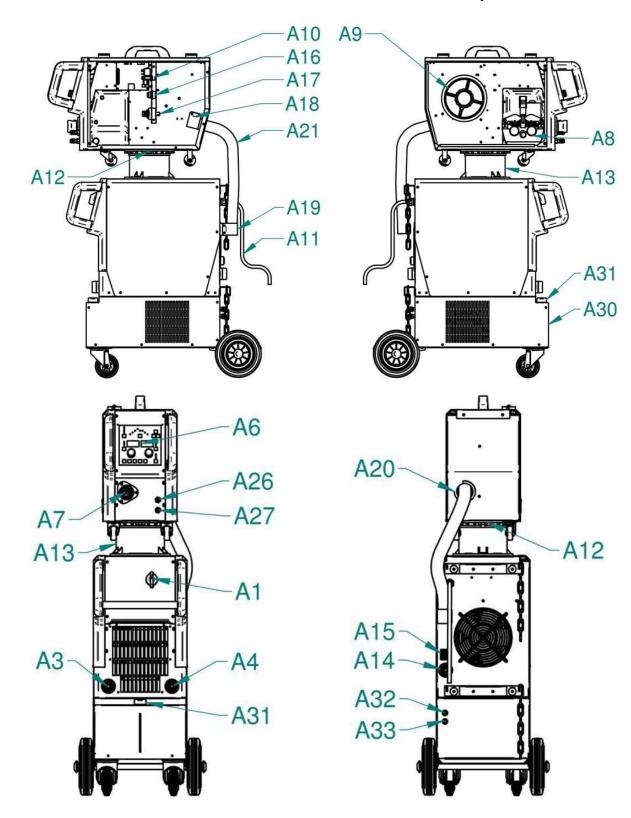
Partes principales de la máquina aXe 400/500 IN
